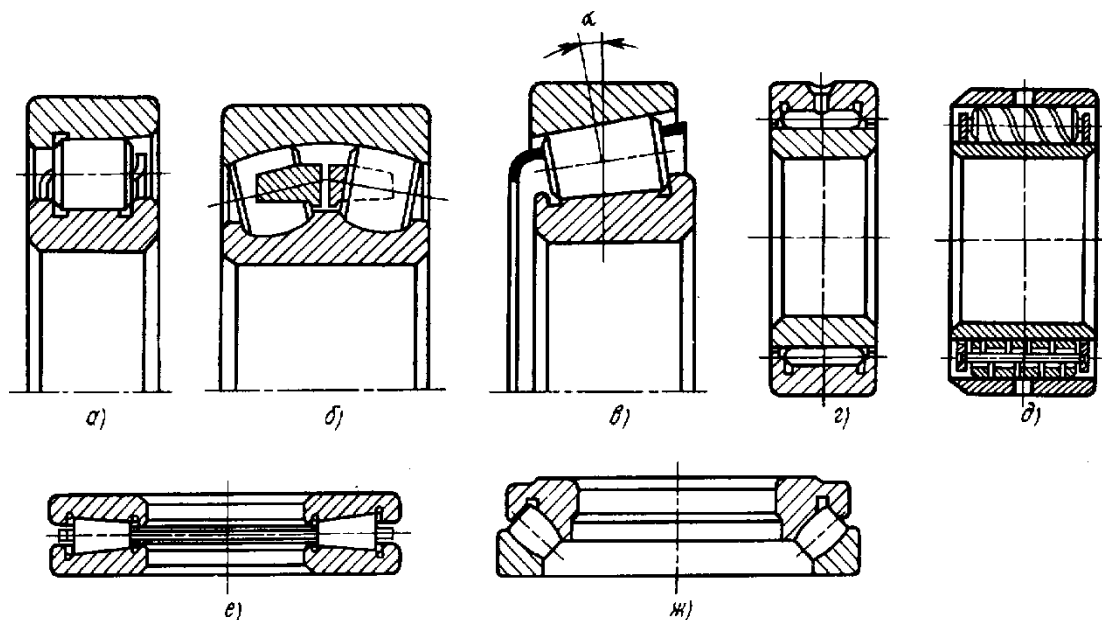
Основные типы роликоподшипников: а – радиальный; б – сферический двухрядный; в – конический радиально-упорный; г – игольчатый; д – с витыми роликами; е – упорно-радиальный; ж - упорный
